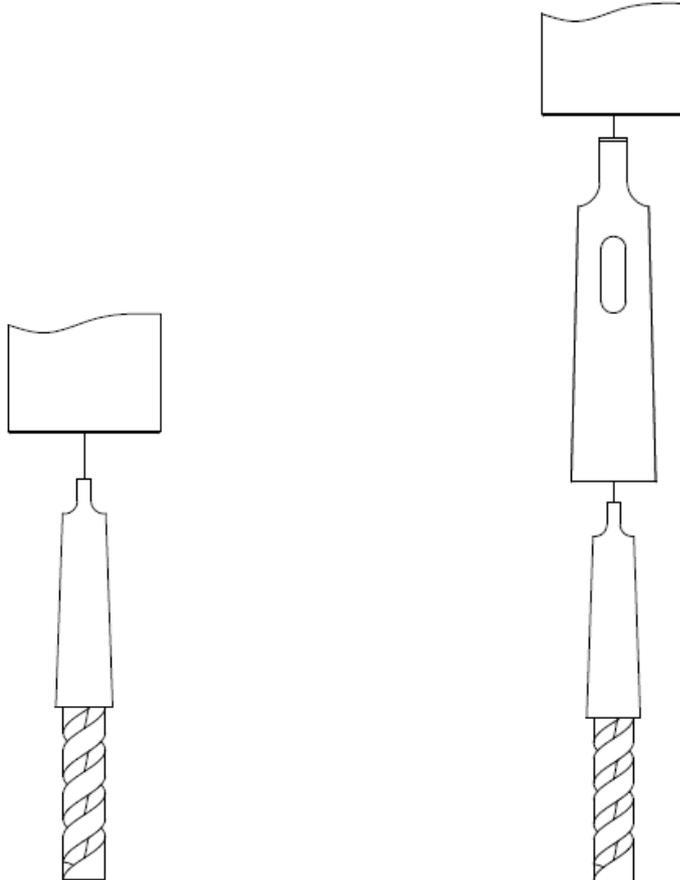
| Beispiel für die Befestigung einer Bohrmaschine mit einem Schlüssel]
